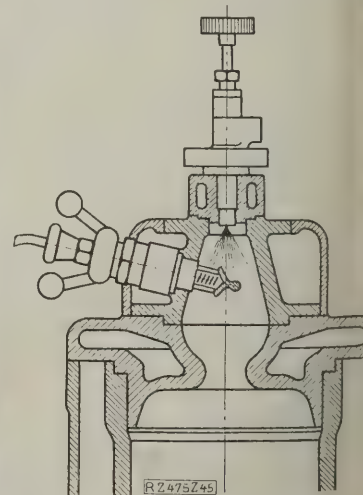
Elektrischer Anlasser, an Glühkopf des Bolindermotors angebaut.
